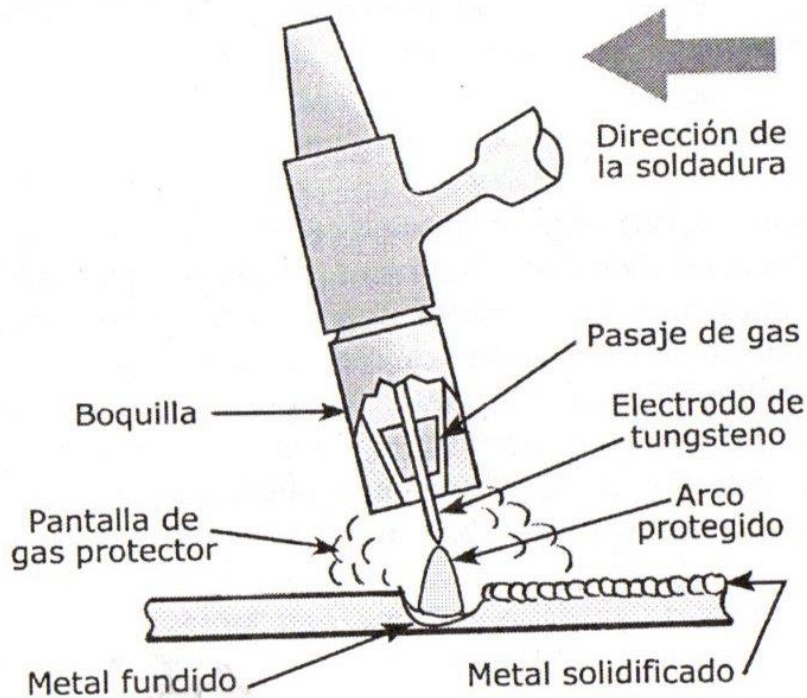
Esquema de un soplete para soldadura TIG
